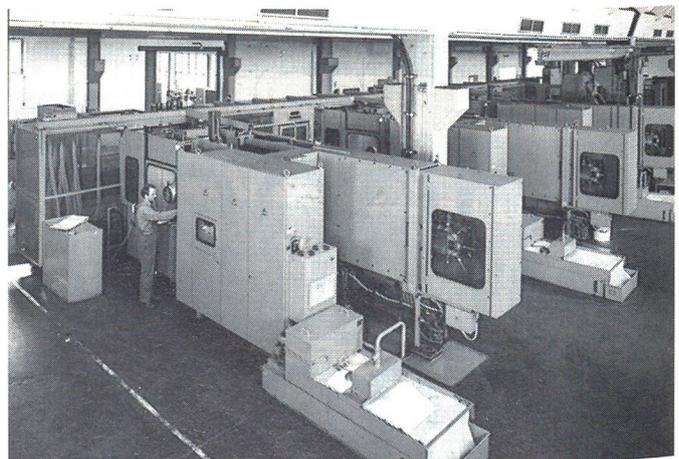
Im Bild drei flexible Fertigungssysteme des hochmodernen Werkzeugmaschinenparks der Universal Maschinenfabrik
